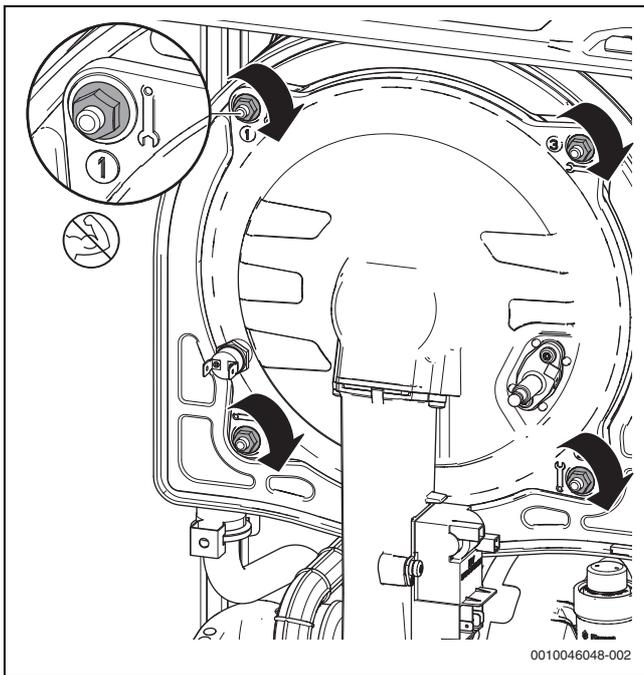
Instalar el módulo de puerta de cámara de combustión en el intercambiador de calor
